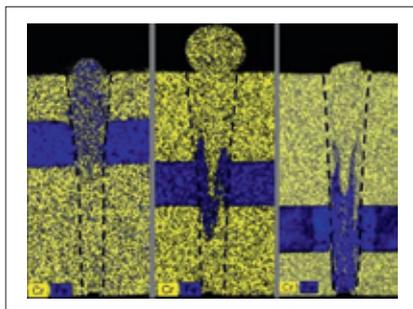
EDX – Aufnahmen von Schweißnahtquerschliffen mit Indikatormaterial
